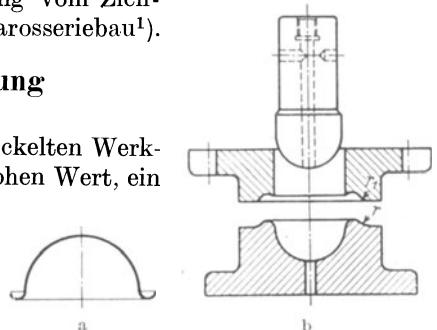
a, b. Werkzeug für Halbkugelformung mit Wulstkante.
